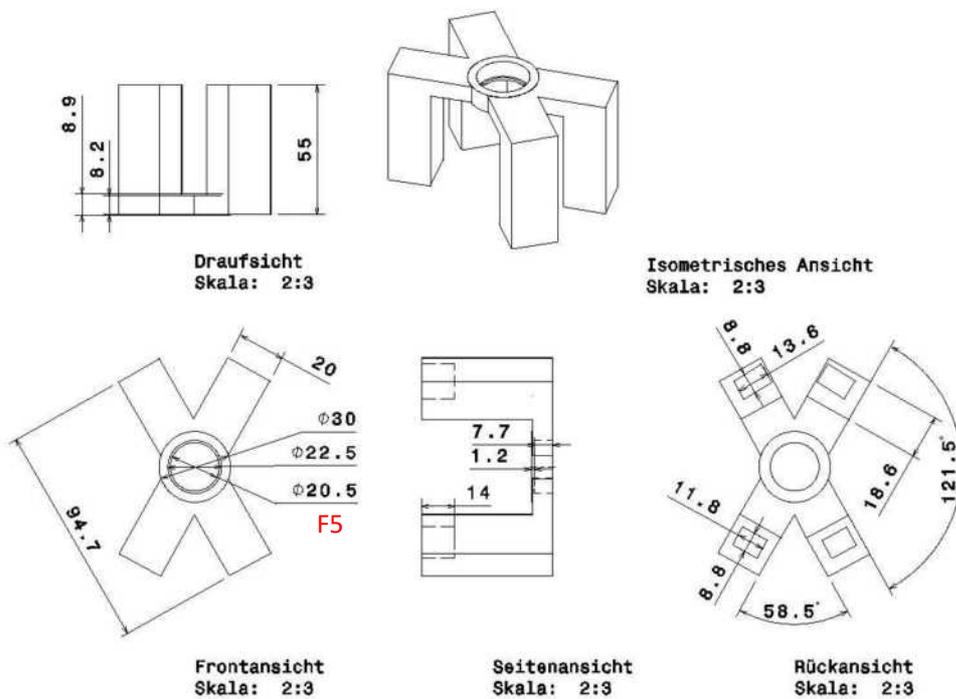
Element 4 (2D-Zeichnung) mit Toleranz
